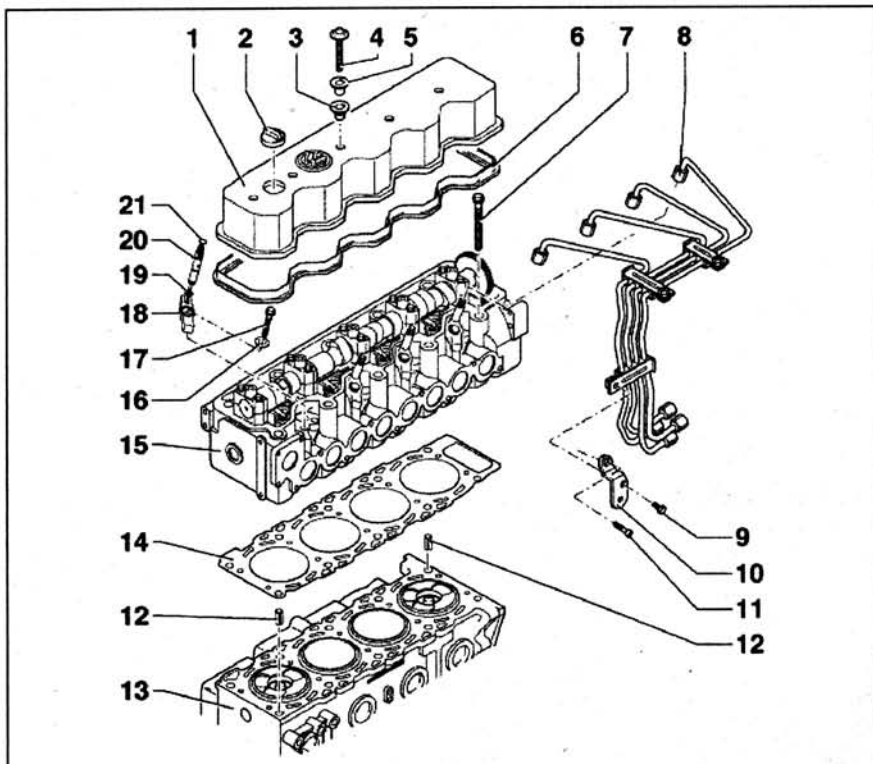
а. Головка блока цилиндров 2.8 TDI:
